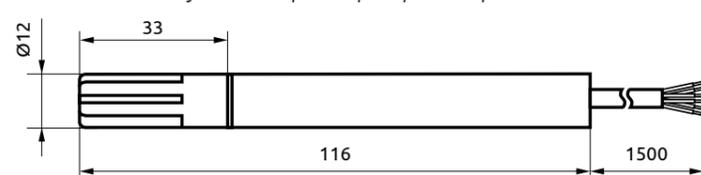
Габаритный размер HTE.PF с кабелем
